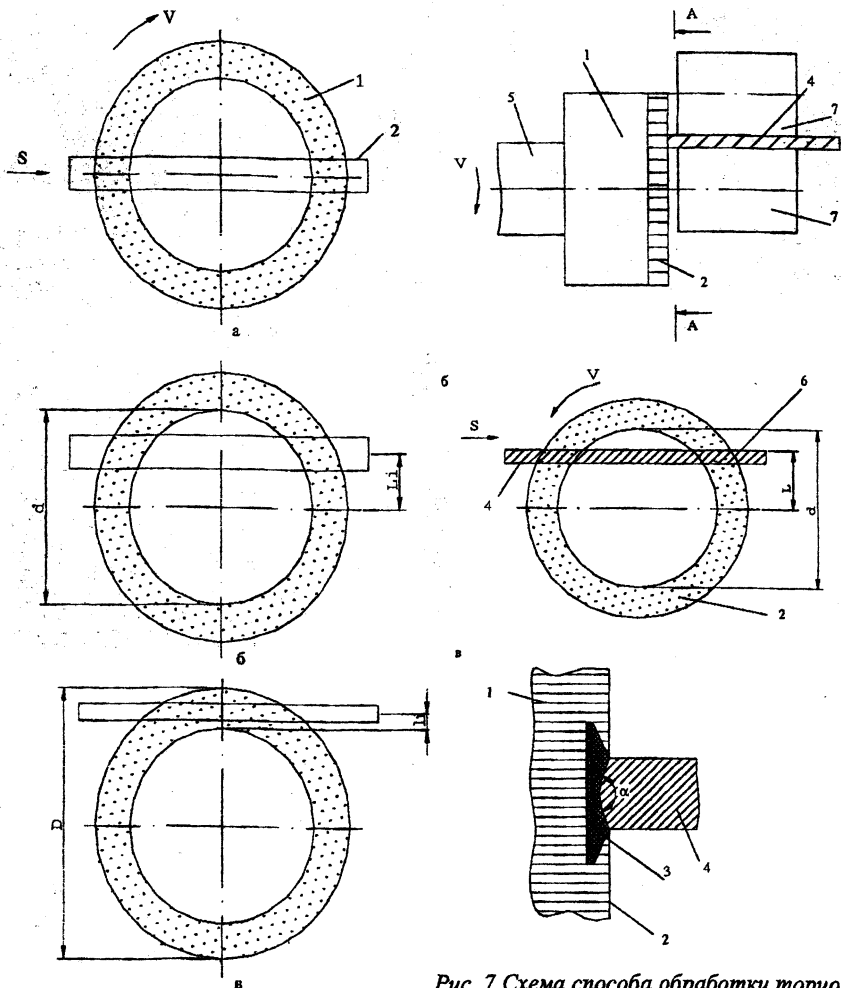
Схемы положения иглофрезы относительно обрабатываемой поверхности:
